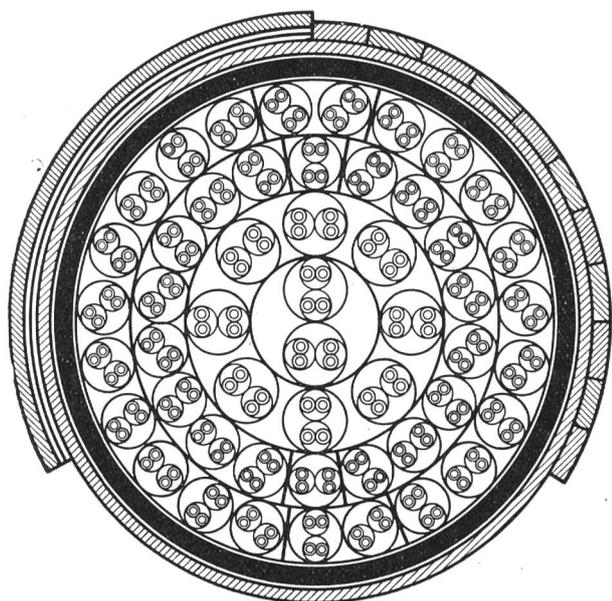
Querschnitt des Kabels mit 51 Vierern.
